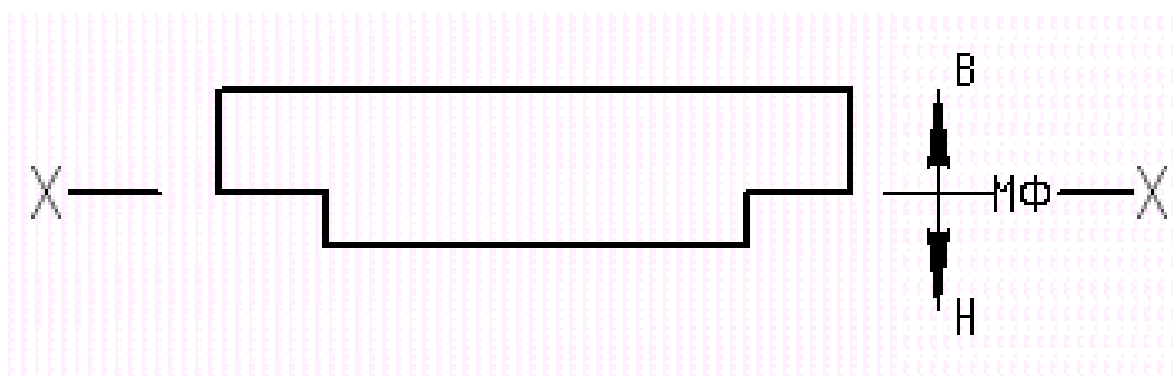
Схема расположения отливки в нижней и верхней полуформах
